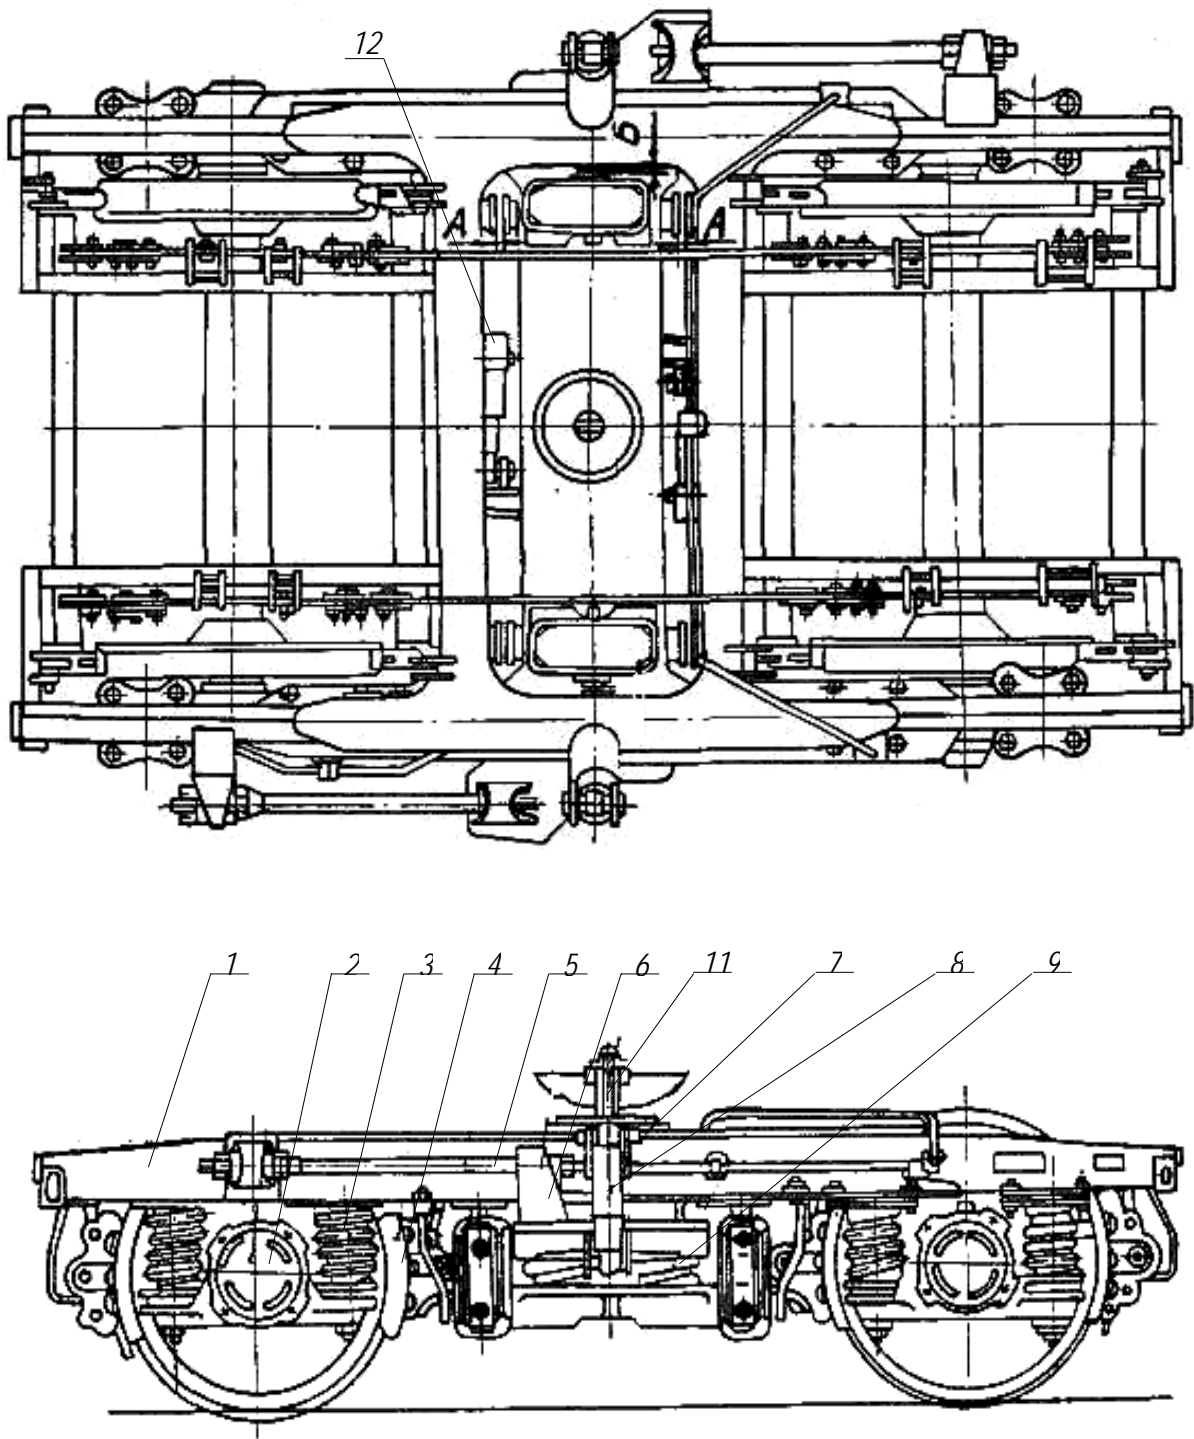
Тележка люлочного типа мод. 68-4065: 1 – рама со шпинтоном, 2 – колесные пары с буксами, 3 – буксовое подвешивание, 4 – тормозная рычажная передача, 5 – поводок, 6 – надрессорный брус, 7 – скользуны, 8 – вертикальный гидравлический гаситель колебаний, 9 – центральное подвешивание, 11 – шкворень, 12 – горизонтальный гидравлический гаситель колебаний
